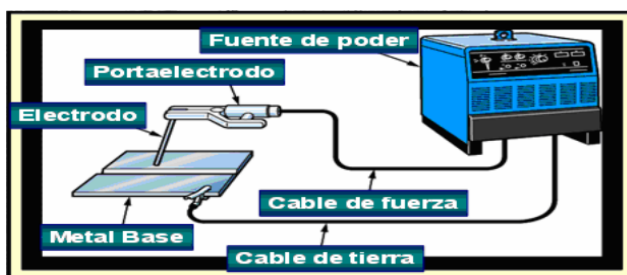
Esquema de la zona de soldadura por fusión [46]
